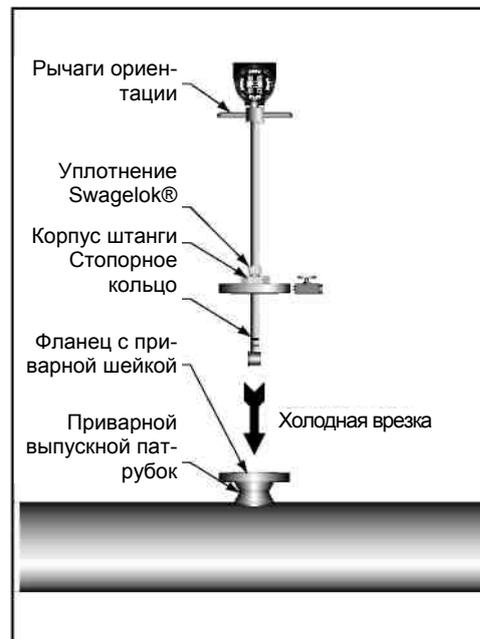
Установка V-Bar-700 с фланцевым присоединением к трубопроводу
